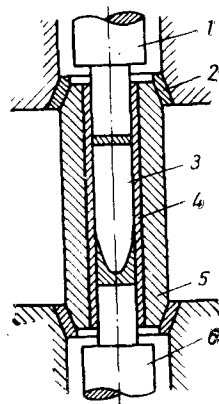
Прессформа для горячего прессования больших сердечников снарядов:
